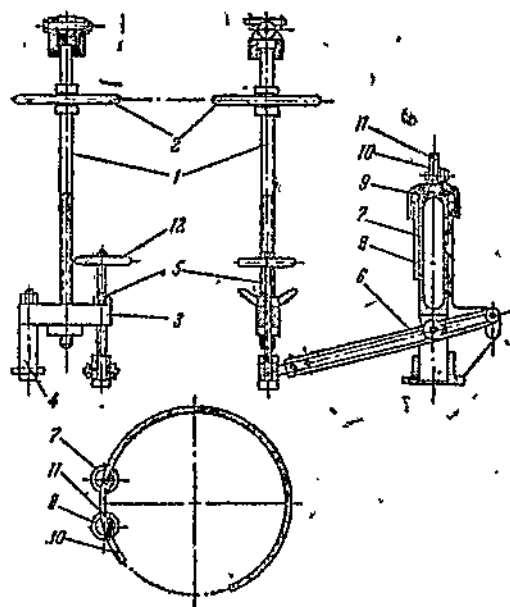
Механизм для регулирования степени наполнения прессовых коробок:
